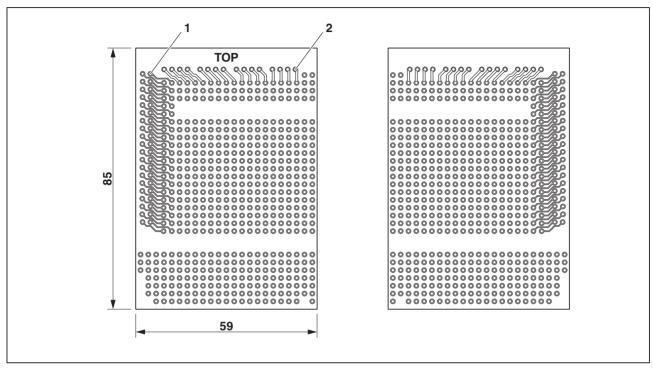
Abmessungen der Leiterplatte RPI-BC INT-PCB SET, 2202994
